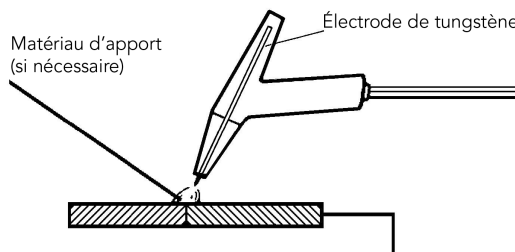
Schéma de principe du soudage TIG.
